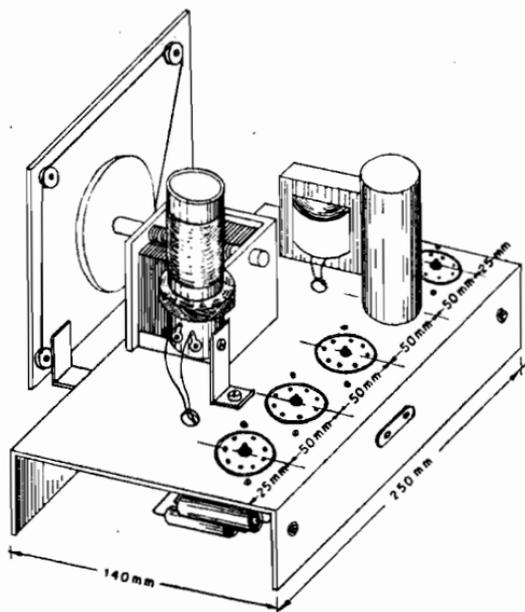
Disposizione delle parti sopra il telaio.
